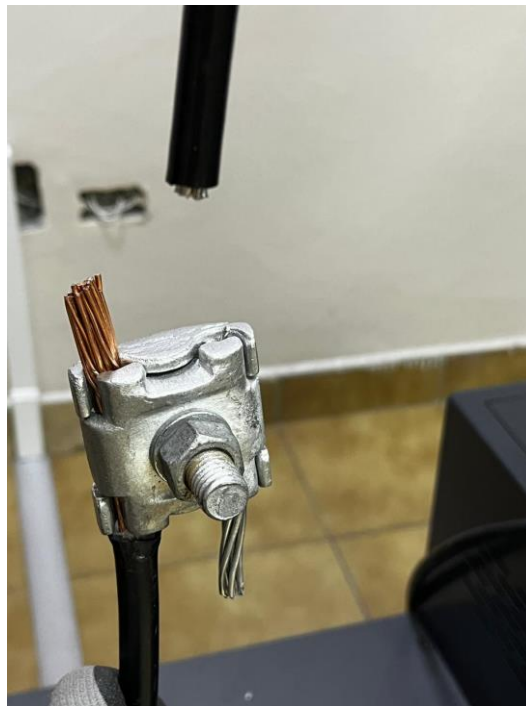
Fractura cortante en el conductor de Aluminio (Al)
